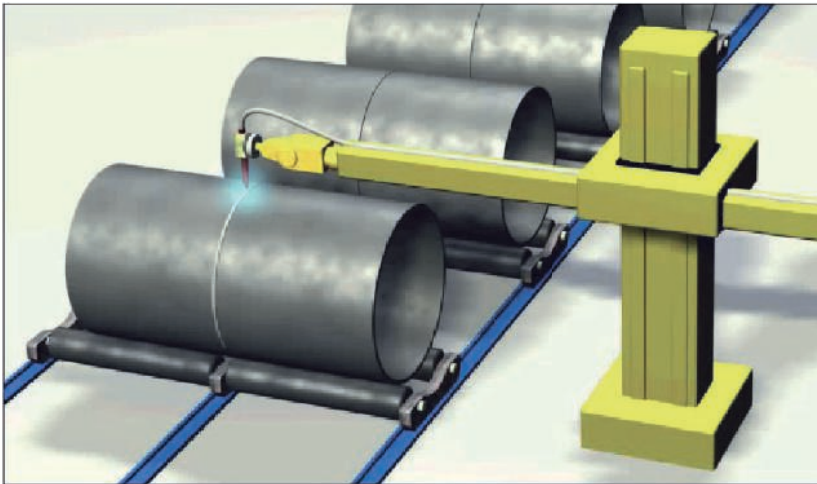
Automatisches Schweißen mit Schweißmast: Sowohl Schweißdrahtzufuhr als auch Schweißbrennerbewegung und Werkstückzufuhr und -bewegung erfolgen mechanisch.
